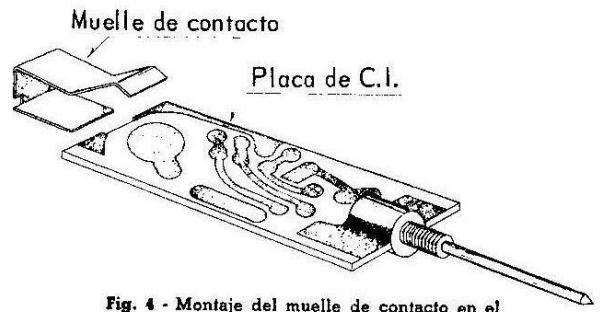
Montaje del muelle de contacto en el circuito impreso.
